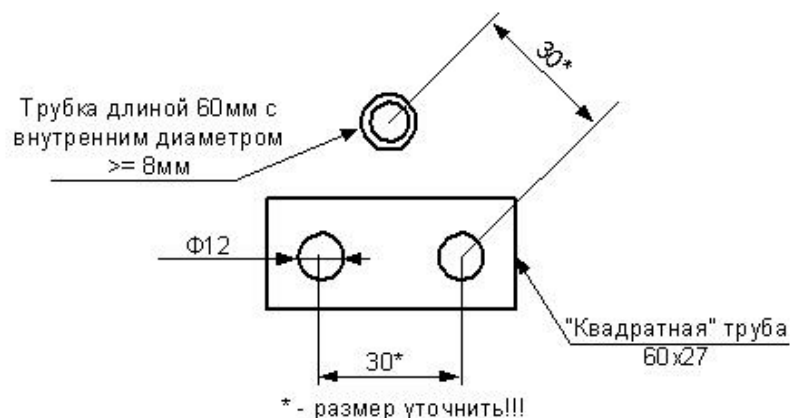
Проставка под платформу рычагов РК (вид сверху).
